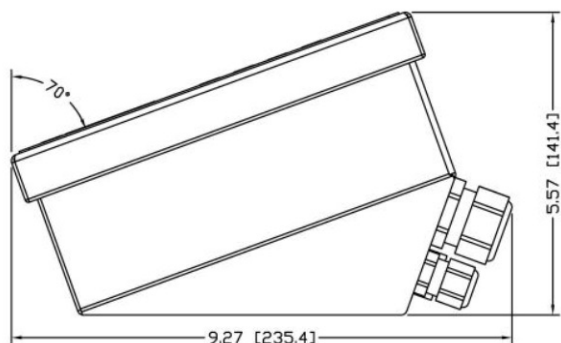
Dimensioni dell'armadietto con montaggio a pannello dell'IND780
